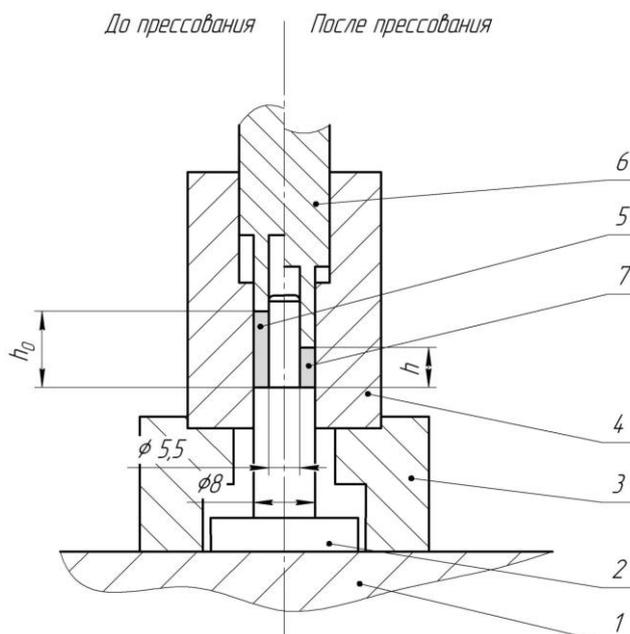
Пресс-инструмент для холодного прессования порошково-гранульной смеси: 1 – стол пресса; 2 – пуансон нижний; 3 – вилка съёмная; 4 – матрица; 5 – порошково-гранульная смесь; 6 – пуансон верхний; 7 – заготовка втулки
